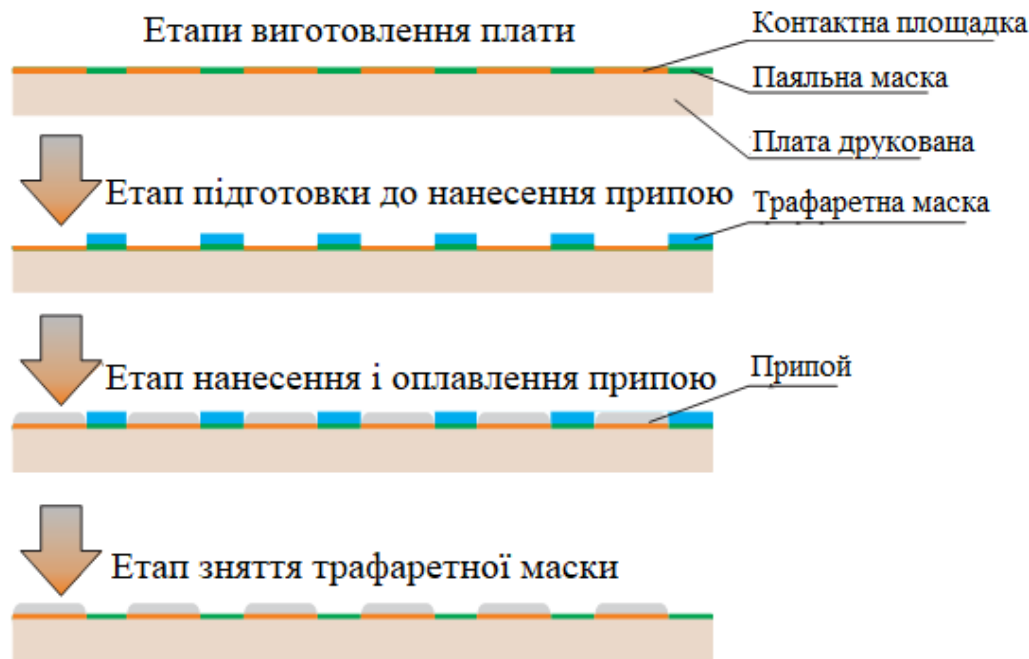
Техпроцес виготовлення ПД Optipad
